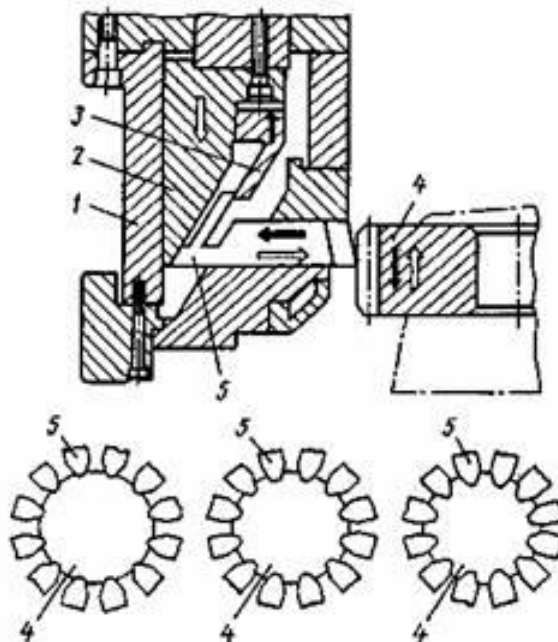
Схема нарезания зубьев резцовой головкой
